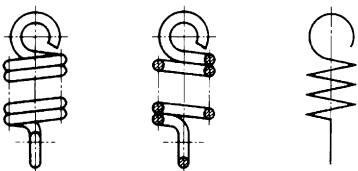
Zylindrische Schrauben-Zugfeder aus Draht mit rundem Querschnitt (DIN 2089, DIN 2097)
